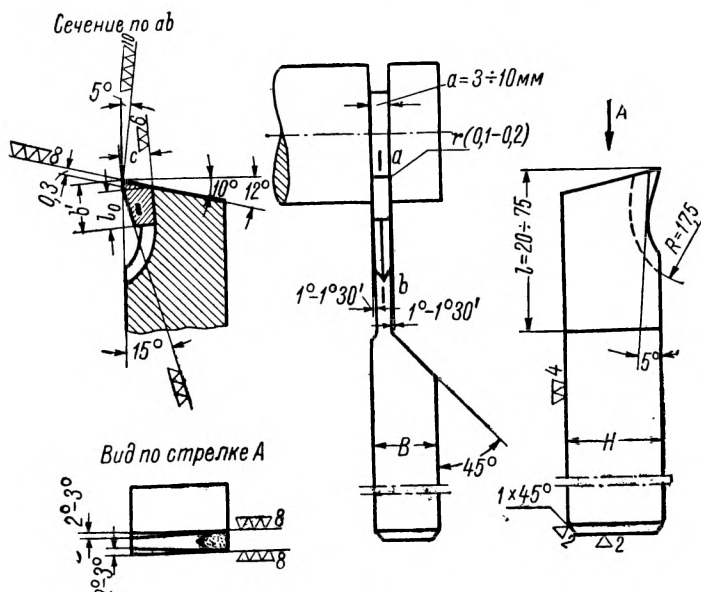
Отрезной резец В. Н. Годяева с клиновидной пластинкой твердого сплава.
